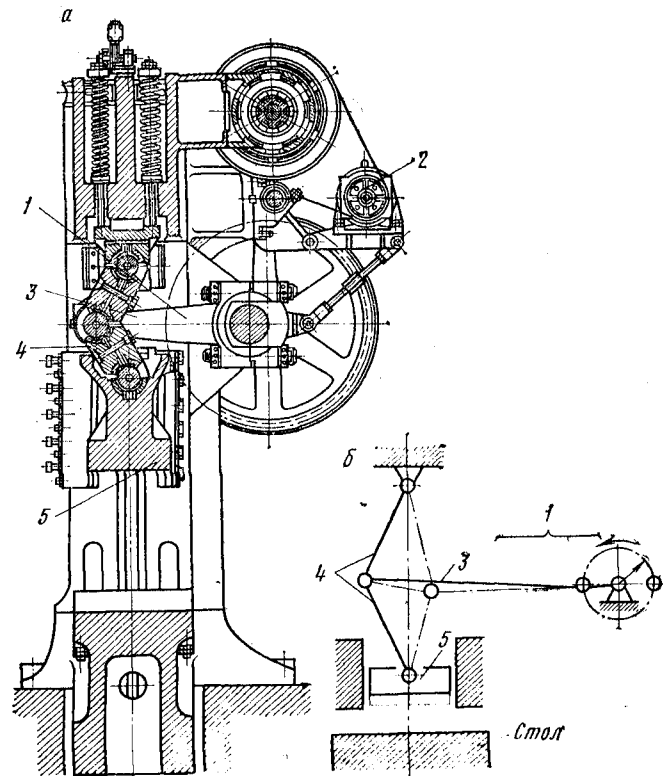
Общий вид (а) и кинематическая схема чеканочного кривошипного прессы (б)
